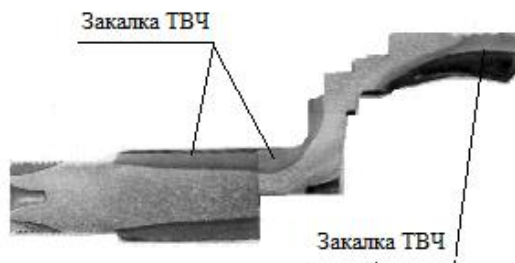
Внешний вид зон закалки ТВЧ на детали корпус шарнира наружный
